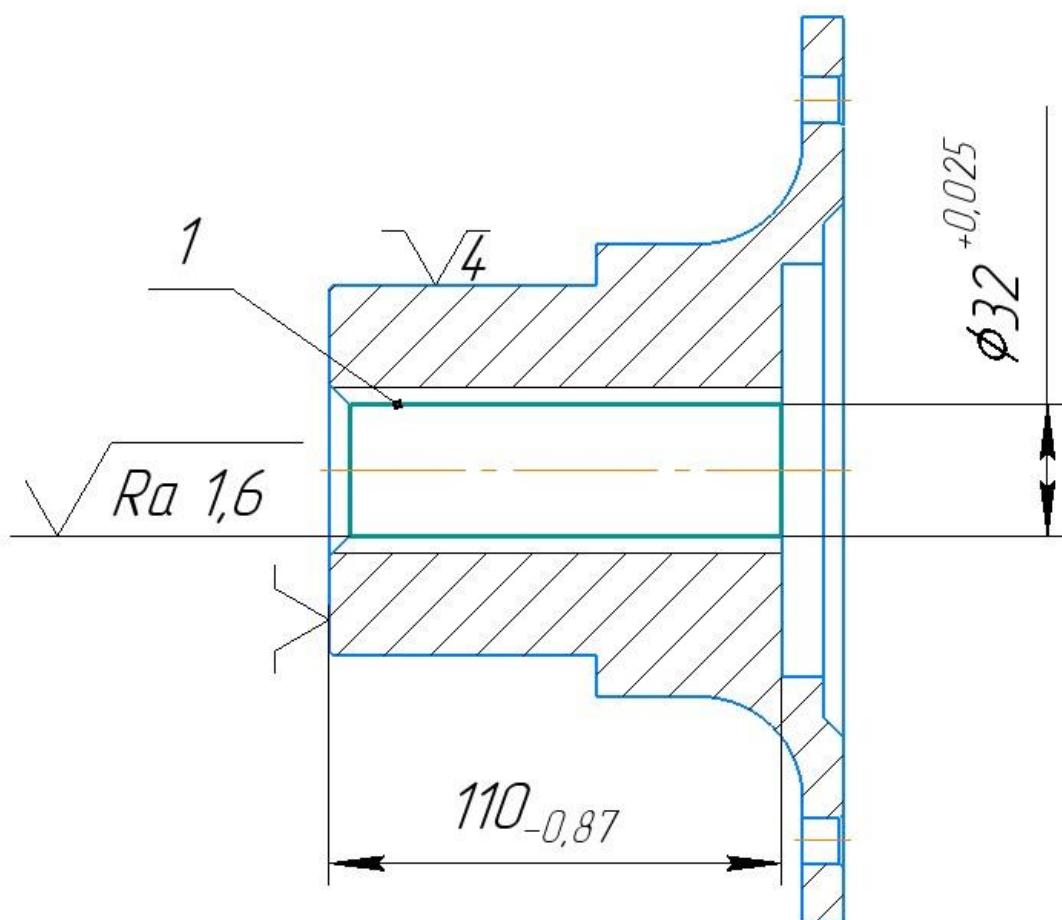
Эскиз операции 090 – Внутришлифовальная
